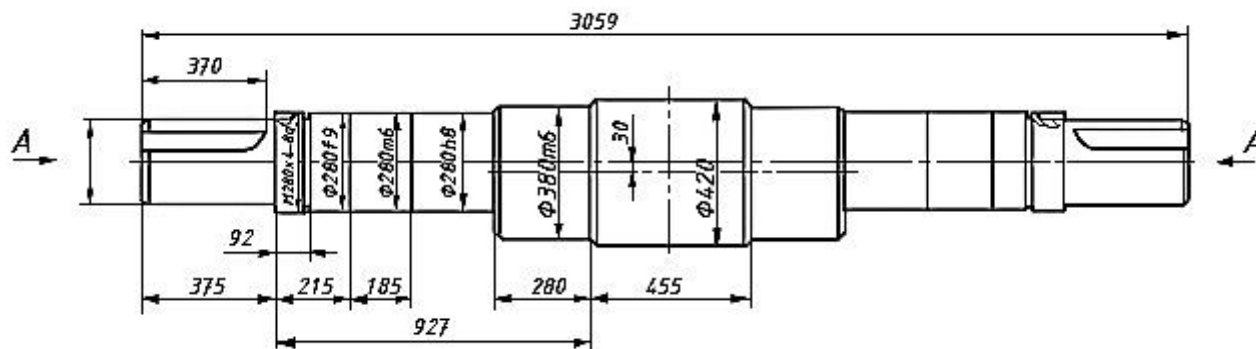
Эскиз эксцентрикового вала щековой дробилки СМД-111
